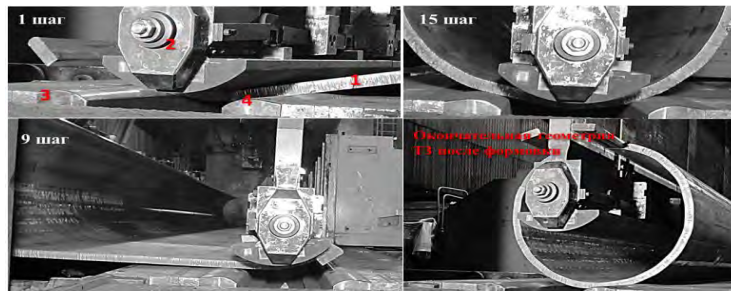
Формовка трубной заготовки на прессе пошаговой формовки по схеме JCOE (1 – трубная заготовка; 2 – пуансон; 3, 4 – бойки)
